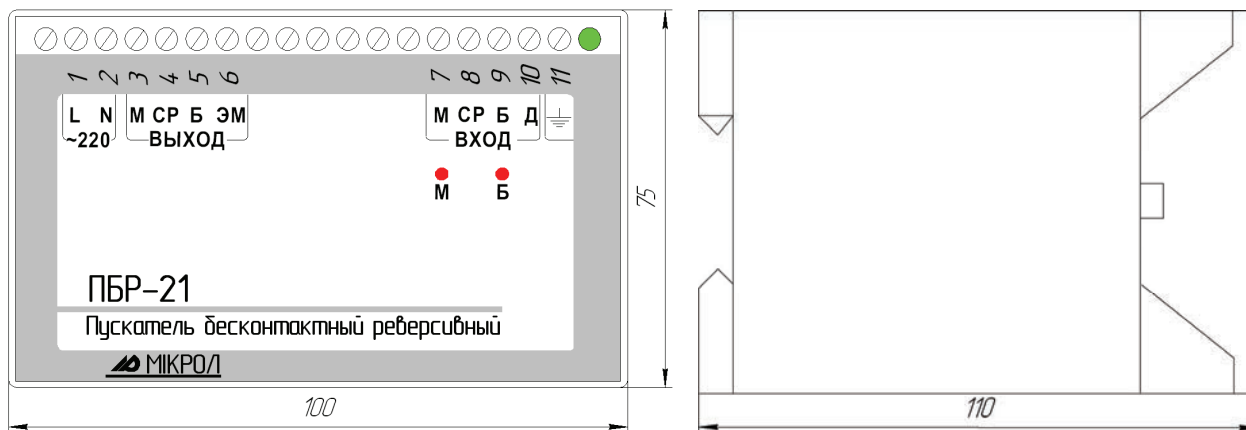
Внешний вид и габаритные размеры преобразователя ПБР-21
